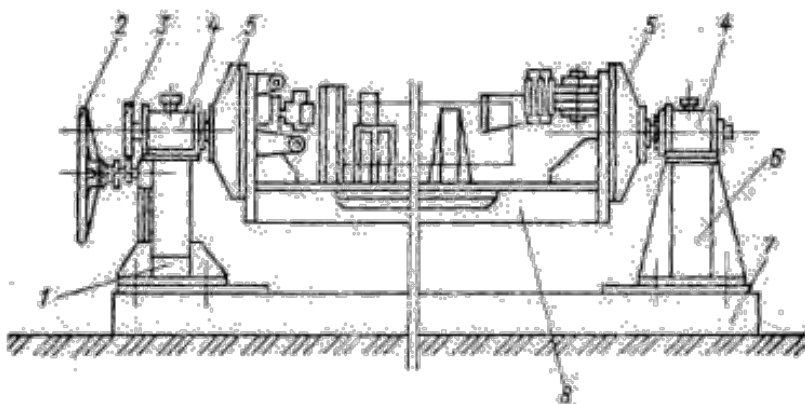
Кондуктор-кантователь для сборки элементов фонарей
